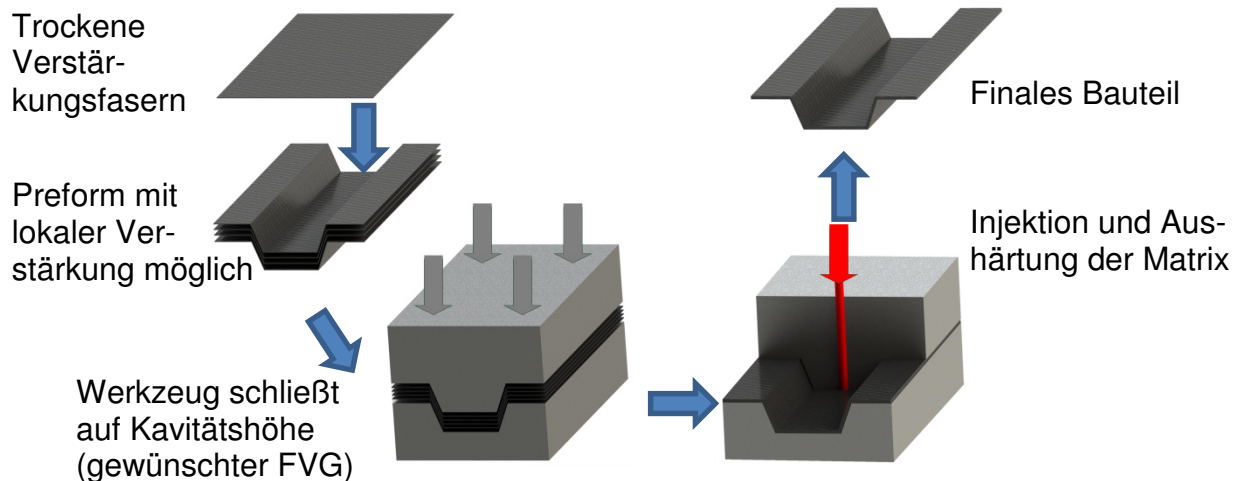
Prozessablauf eines Resin Transfer Molding (RTM) Prozesses
